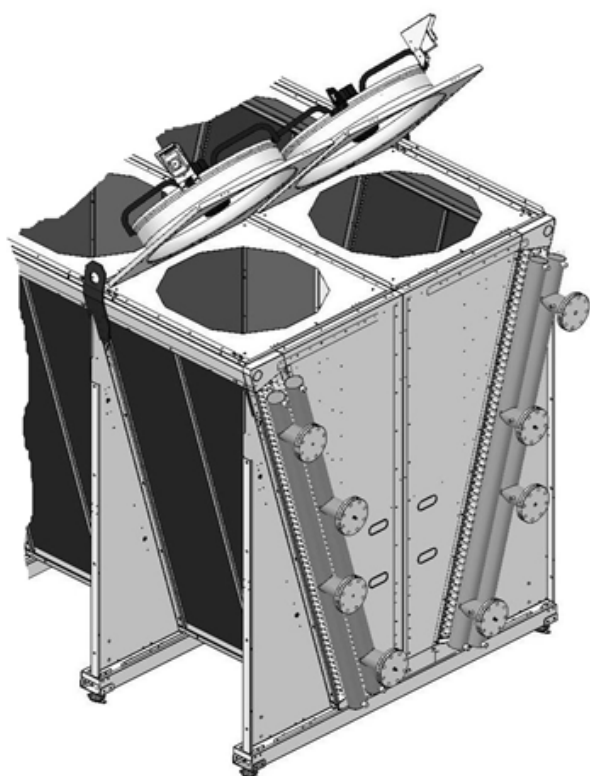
Prima di aprire, sezionare l'alimentazione del motventilatore. Rimuovere le viti di fissaggio del convogliatore apribile. Attenzione che diventa accessibile la zona interna: pericolo di caduta nel vano sottostante, pericolo di taglio sul pacco alettato, pericolo con il rotore del motoventilatore non protetto, pericolo di schiacciamento degli arti in fase di apertura o chiusura del convogliatore.
